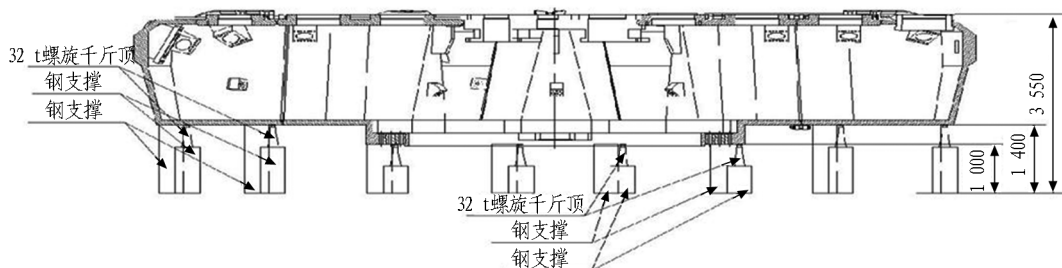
刀盘现场组焊布置示意图(单位: mm)
